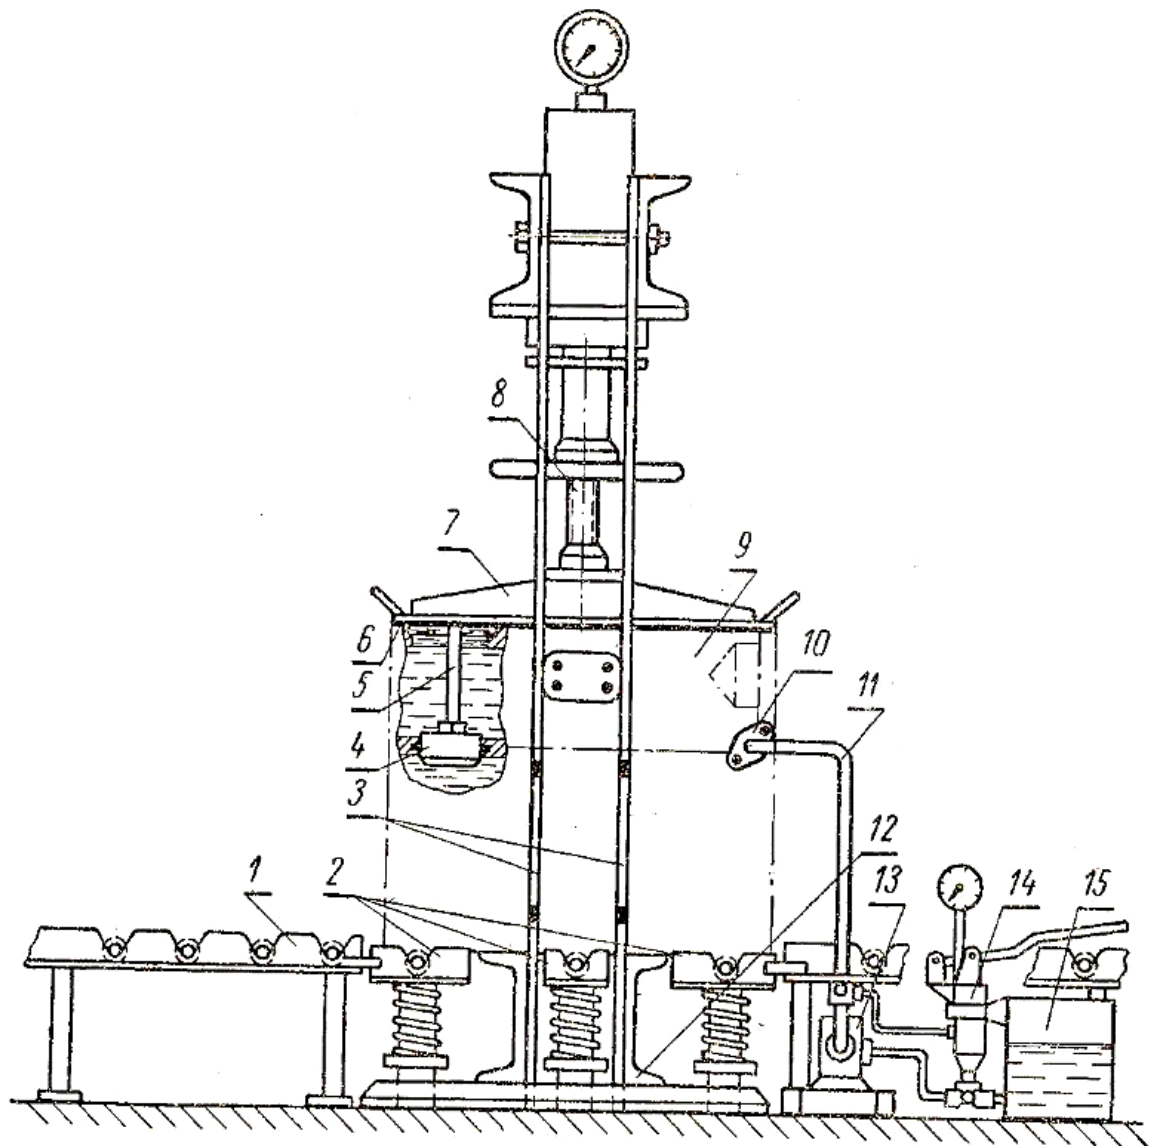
Стенд для гідравлічного випробування блоків циліндрів двигуна: 1 - секція рольганга; 2 - підпружинені секції рольганга; 3 - пластини стійок преса; 4 - пробка; 5 - штанга; 6 - прокладка; 7 - плита; 8 - шток преса; 9 - блок циліндрів; 10 - заглушка з патрубком; 11 - шланг для підведення и відведення води; 12 - стіл преса (швелер); 13 - відцентровий насос; 14 - ручний насос; 15 - бак з водою
